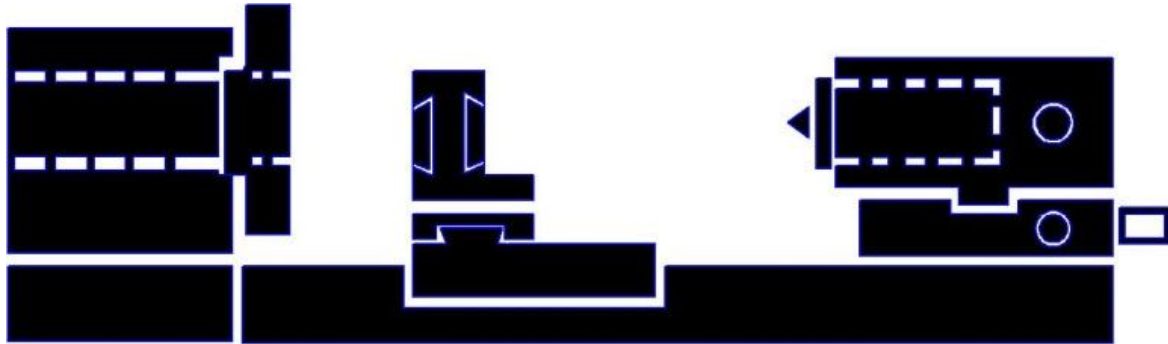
Головний вид важкого токарного верстата базової конструкції
